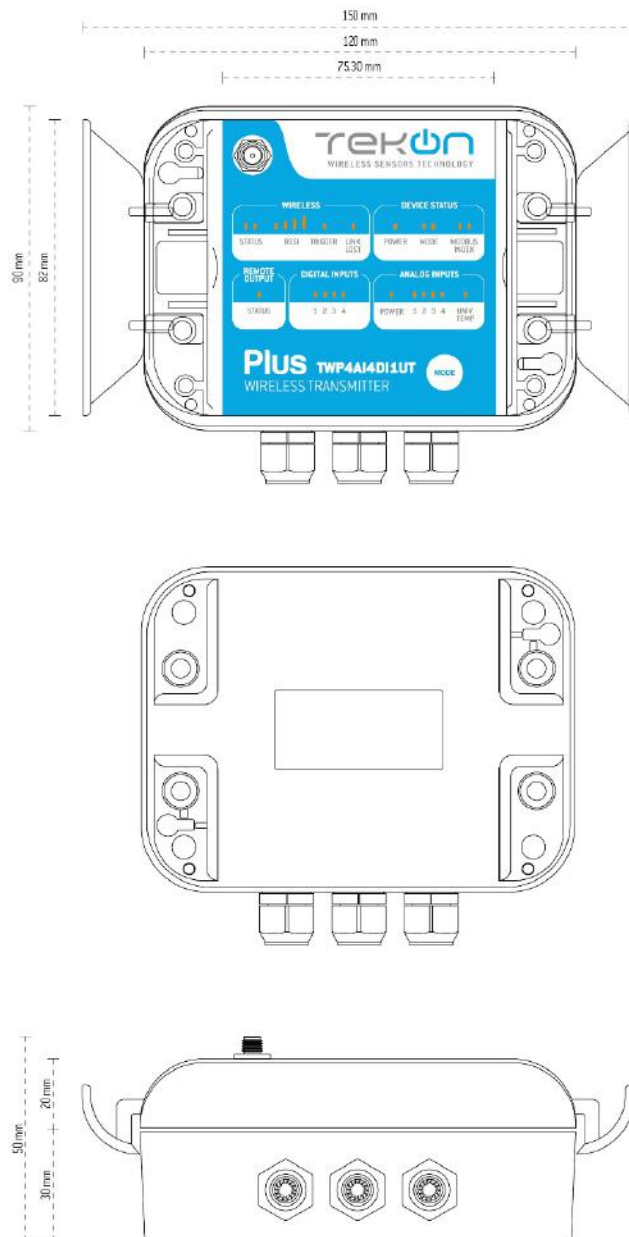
Dimensões e interface mecânica do transmissor TWP-4AI4DI1UT
